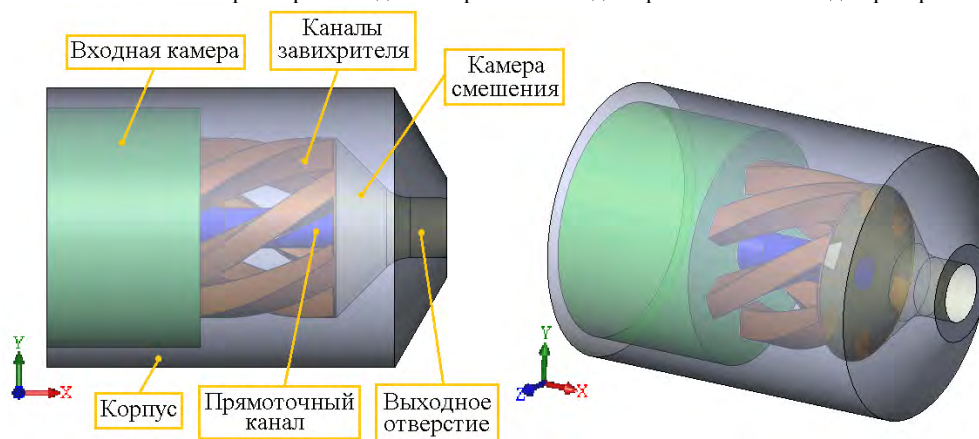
Трехмерный вид геометрической модели прямоточно-вихревой форсунки
